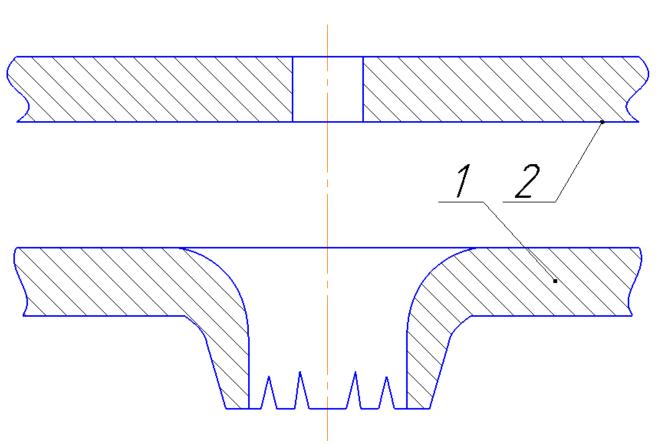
Получение отверстия с отбортовкой с использованием предварительной пробивки [9]: 1 – заготовка с предварительно пробитым отверстием; 2 – заготовка с отверстием с отбортовкой
